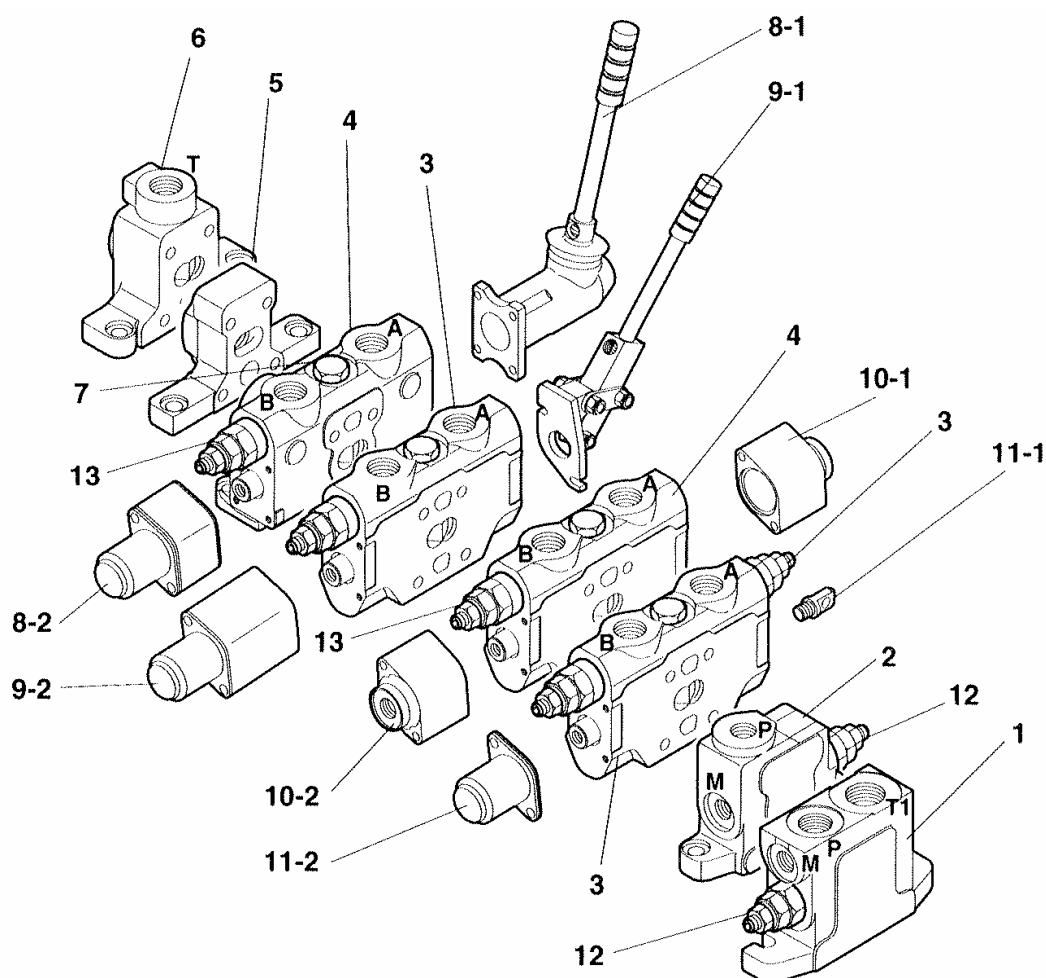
Horizontálně sestavený blok SB23 OC prvků mobilní hydrauliky (Rexroth Bosch Group)
